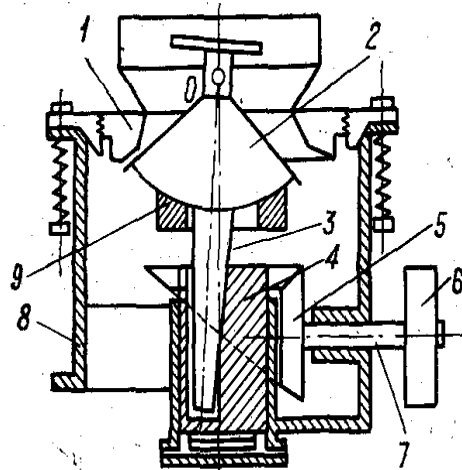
Схема конусной дробилки для среднего дробления с валом, подвешенным на сферическом подпятнике: 1 – коническая чаша; 2 – дробящий конус; 3 – вал; 4 – эксцентриковый стакан; 5 – коническая передача; 6 – шкив; 7 – приводной вал; 8 – станина; 9 – подпятник
